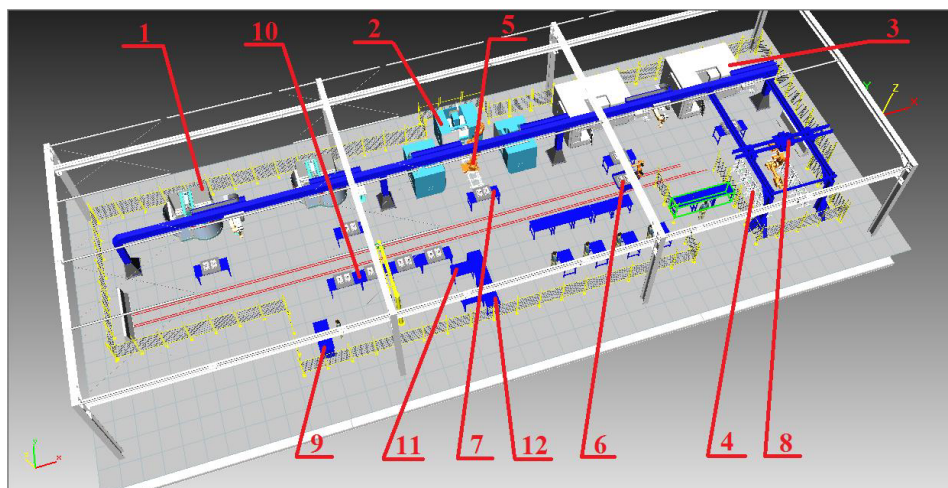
Виртуальная планировка автоматизированного участка обработки группы деталей типа «диск»: 1-токарно-винторезный ГПМ на базе станка мод. 1SE520; 2-вертикально-фрезерный ГПМ на базе станка мод. F100, 3-круглошлифовальный ГПМ на базе станка мод. MKS 1332; 4-склад; 5-манипулятор; 6-транспортная тележка; 7-накопитель; 8-кран штабелер; 9-слесарный верстак; 10-накопитель; 11-стелаж приспособлений, 12-стелаж инструмента
